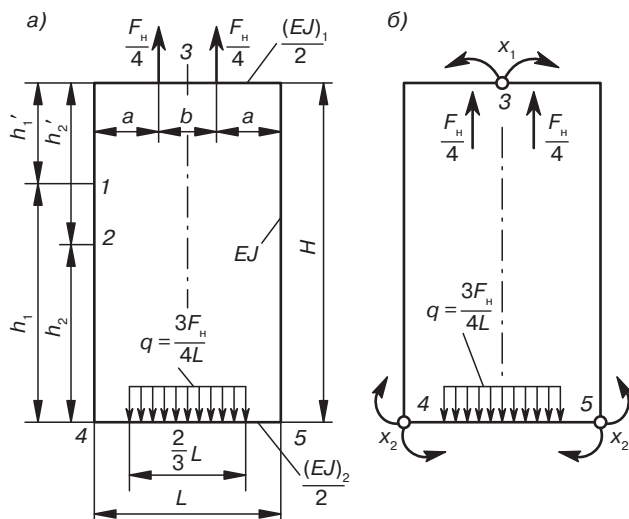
Расчетная схема станины одноцилиндрового колонного прессы: а — схема нагружения; б — схема врезки шарниров
